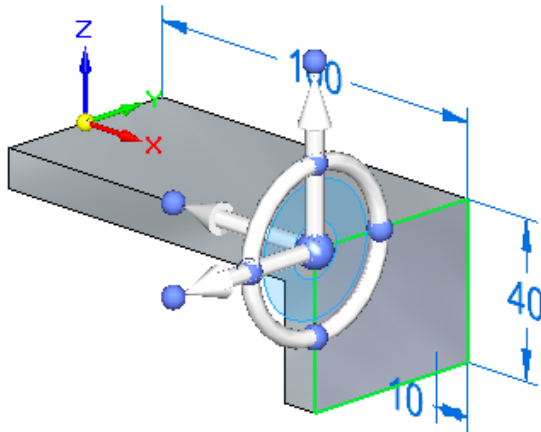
Steuerrad an einem Eckpunkt der Fläche
